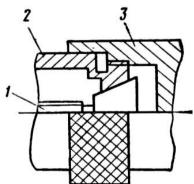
Микрометр завода «Красный инструментальщик»: 1 — микровинт; 2—барабан; 3 — корпус трещотки
